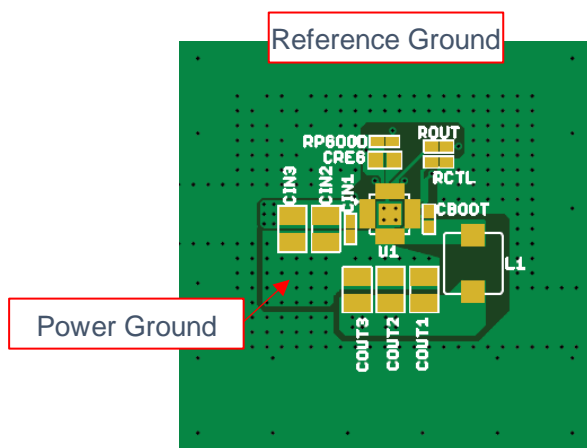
PCB レイアウト例 (降圧 DC/DC コンバータ)
